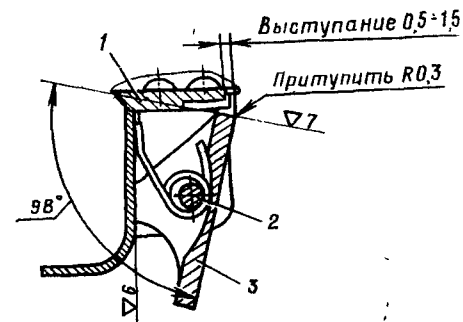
Подгонка защелки магазина: 1 — ствольная коробка; 2 — ось защелки магазина; 3 — защелка магазина
